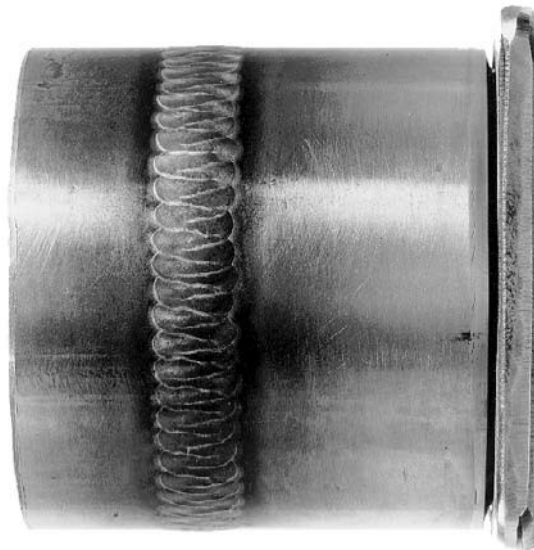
Solda Oscilante de um Tampão de Tubulação.
